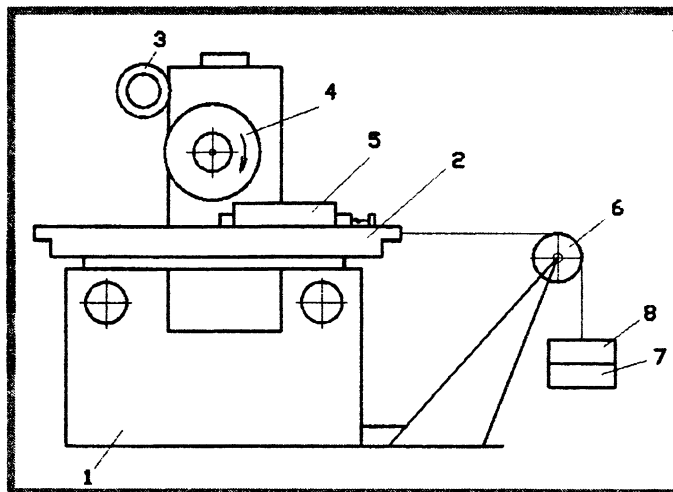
Схема наладки станка 3Е642 для проведения испытаний: 1 – станок; 2 – стол продольный; 3 – привод; 4 – испытываемый круг; 5 – образец из хрусталя; 6 – блок; 7 – уравнивающий груз; 8 – рабочая нагрузка
